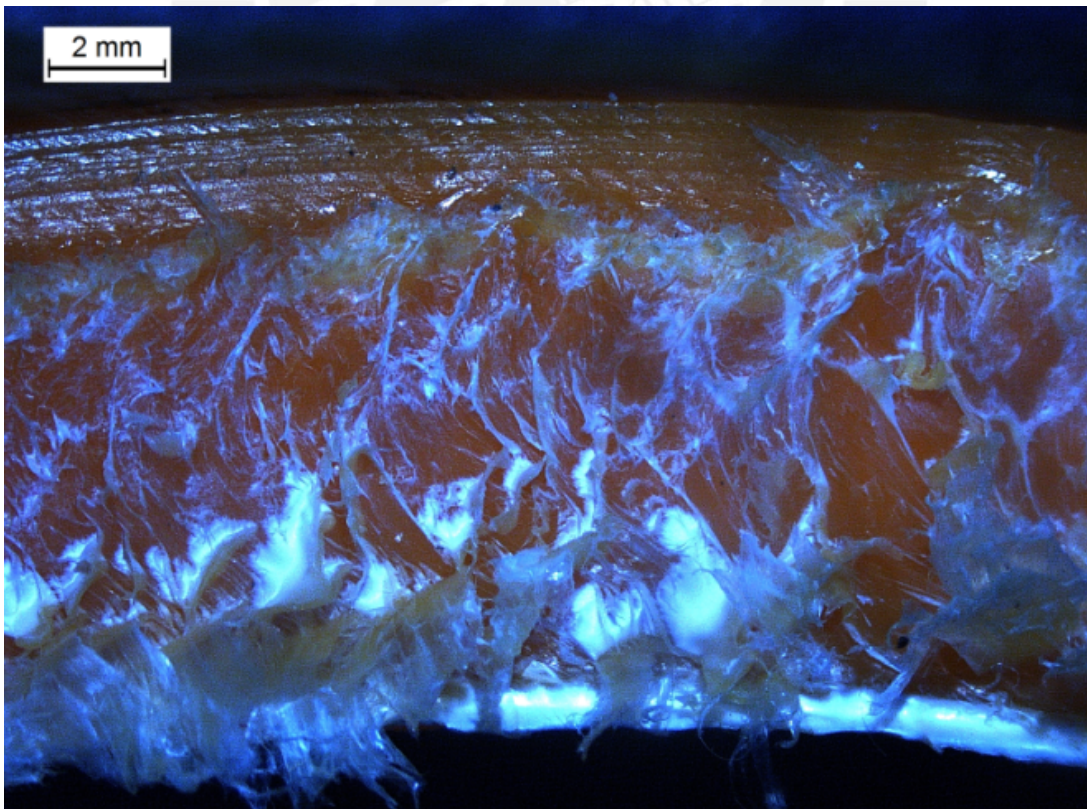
Superficie de fractura soldadura a 600 RPM, probeta 600-2
